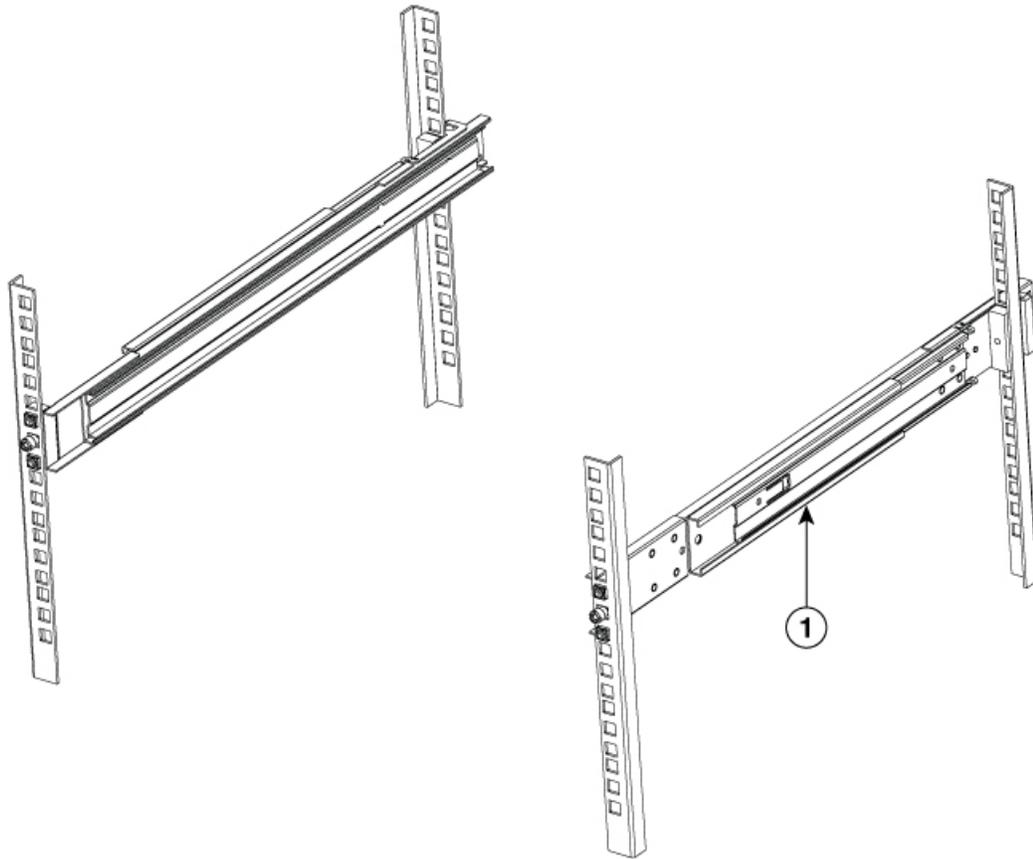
Extrémités arrière et avant (NC55-2RU-ACC-SL2) du rail coulissant externe
